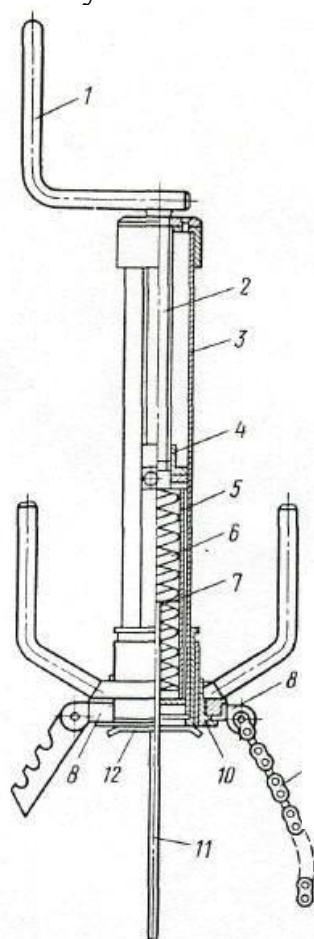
Прибор для измерения глубины загнивания древесины с помощью иглы: 1 – ручка, 2 – винт, 3 – корпус, 4, 10 – гайки, 5 – внутренний цилиндр, 6 – пружина, 7 – указатель, 8 – ушки, 9 – цепь, 11 – игла, 12 – упор
